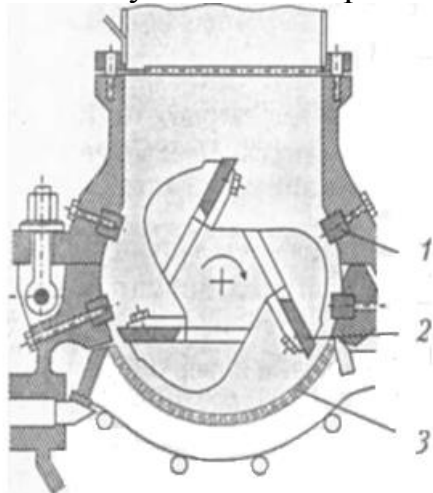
Ножевая дробилка: 7 – неподвижный нож; 2 – подвижный нож; 3 – сито.
